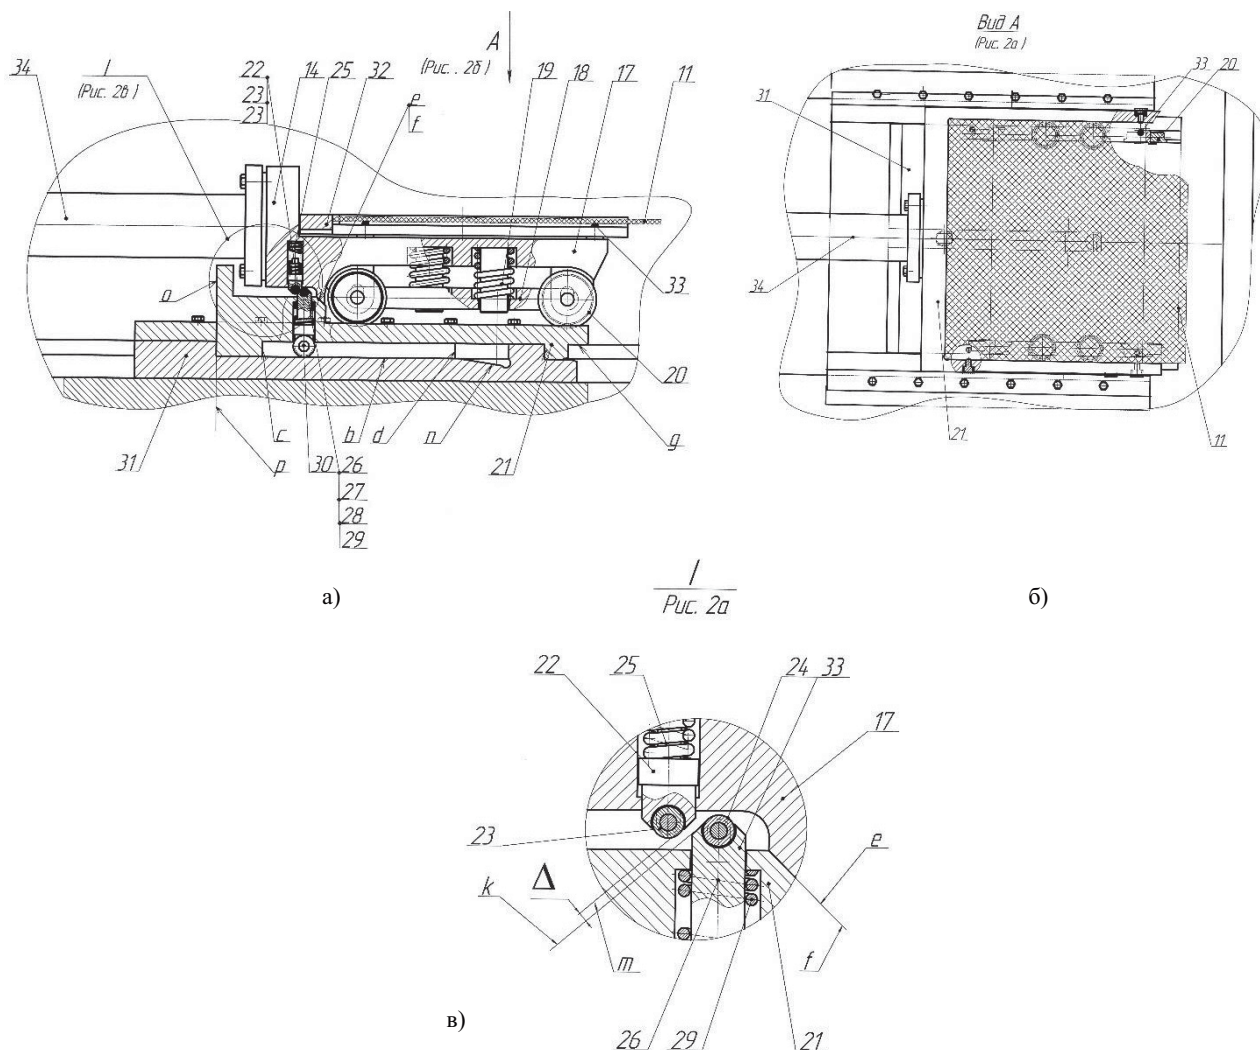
Схема конструктивного исполнения устройства подачи-удаления крупногабаритных заготовок в зону штамповки и обратно:
